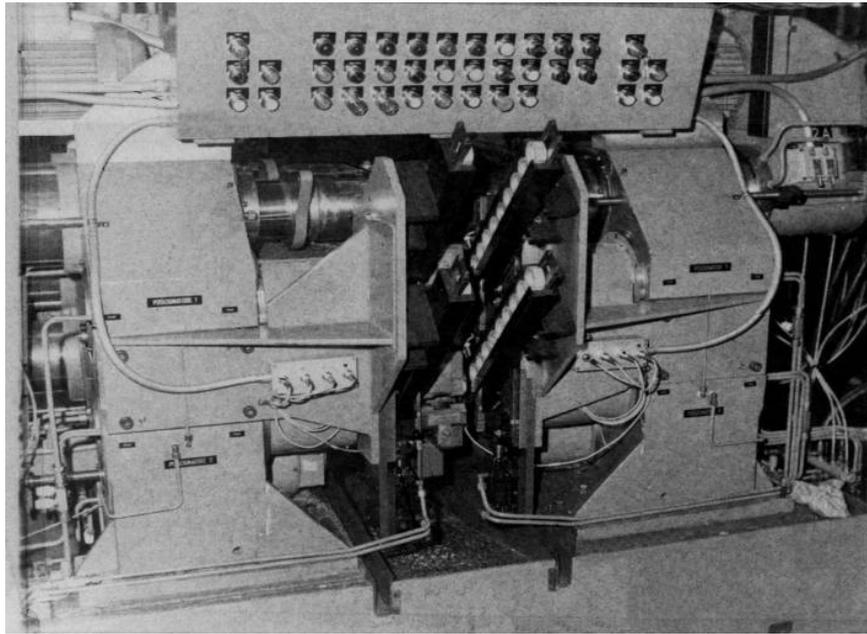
Câmara de Usinagem do Torno CNC
